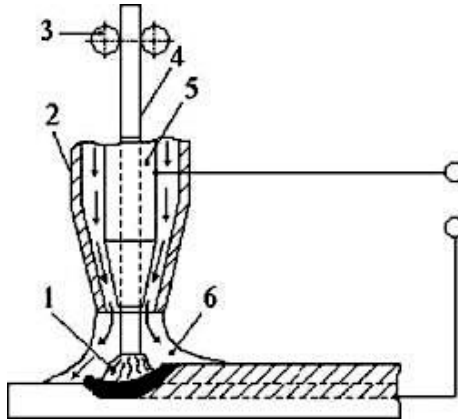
Схема дуговой сварки в защитном газе плавящимся электродом:
